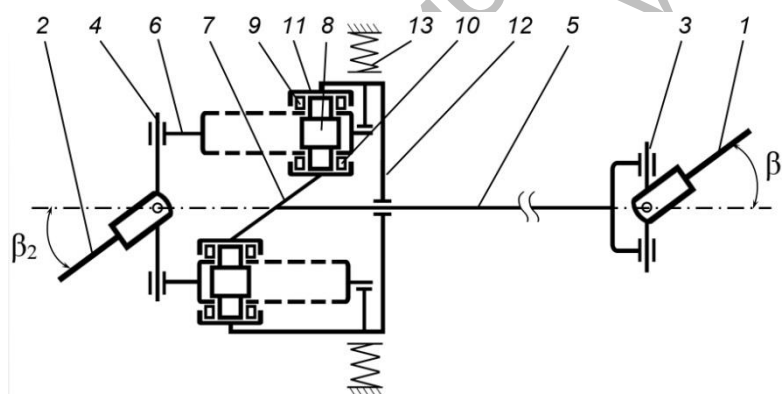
Кинематическая схема двухшарнирного приводного вала
